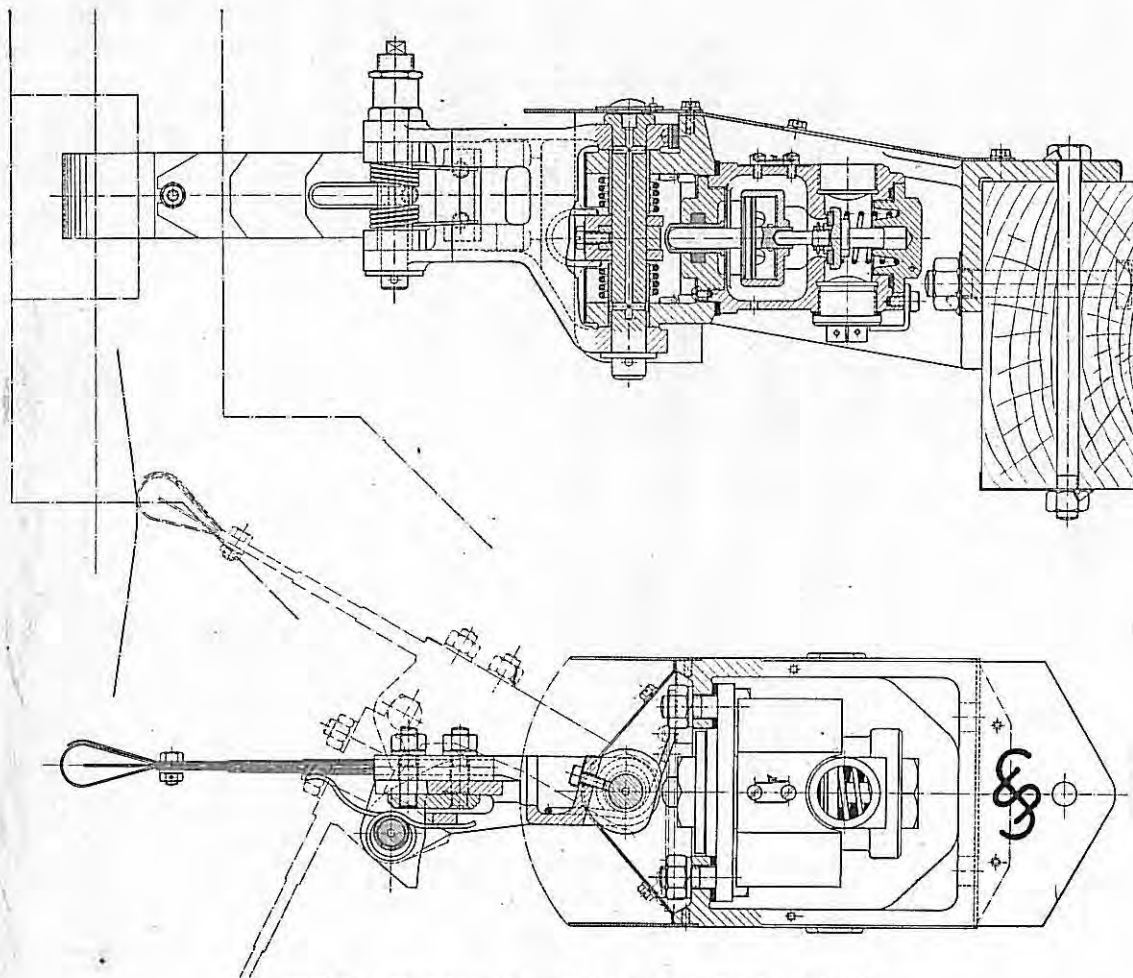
Auslöseventil der Fahrsperrung mit Fahrsperrhebel
